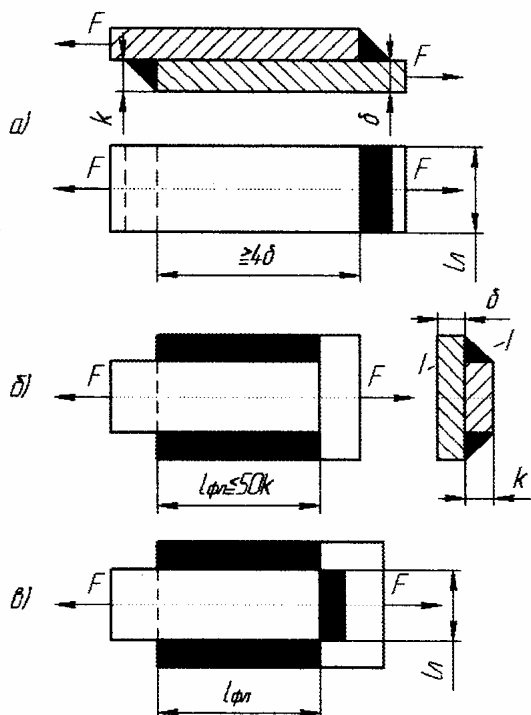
К расчету нахлесточных сварных соединений угловыми швами: а – лотовыми; б – фланговыми; в – комбинированными
